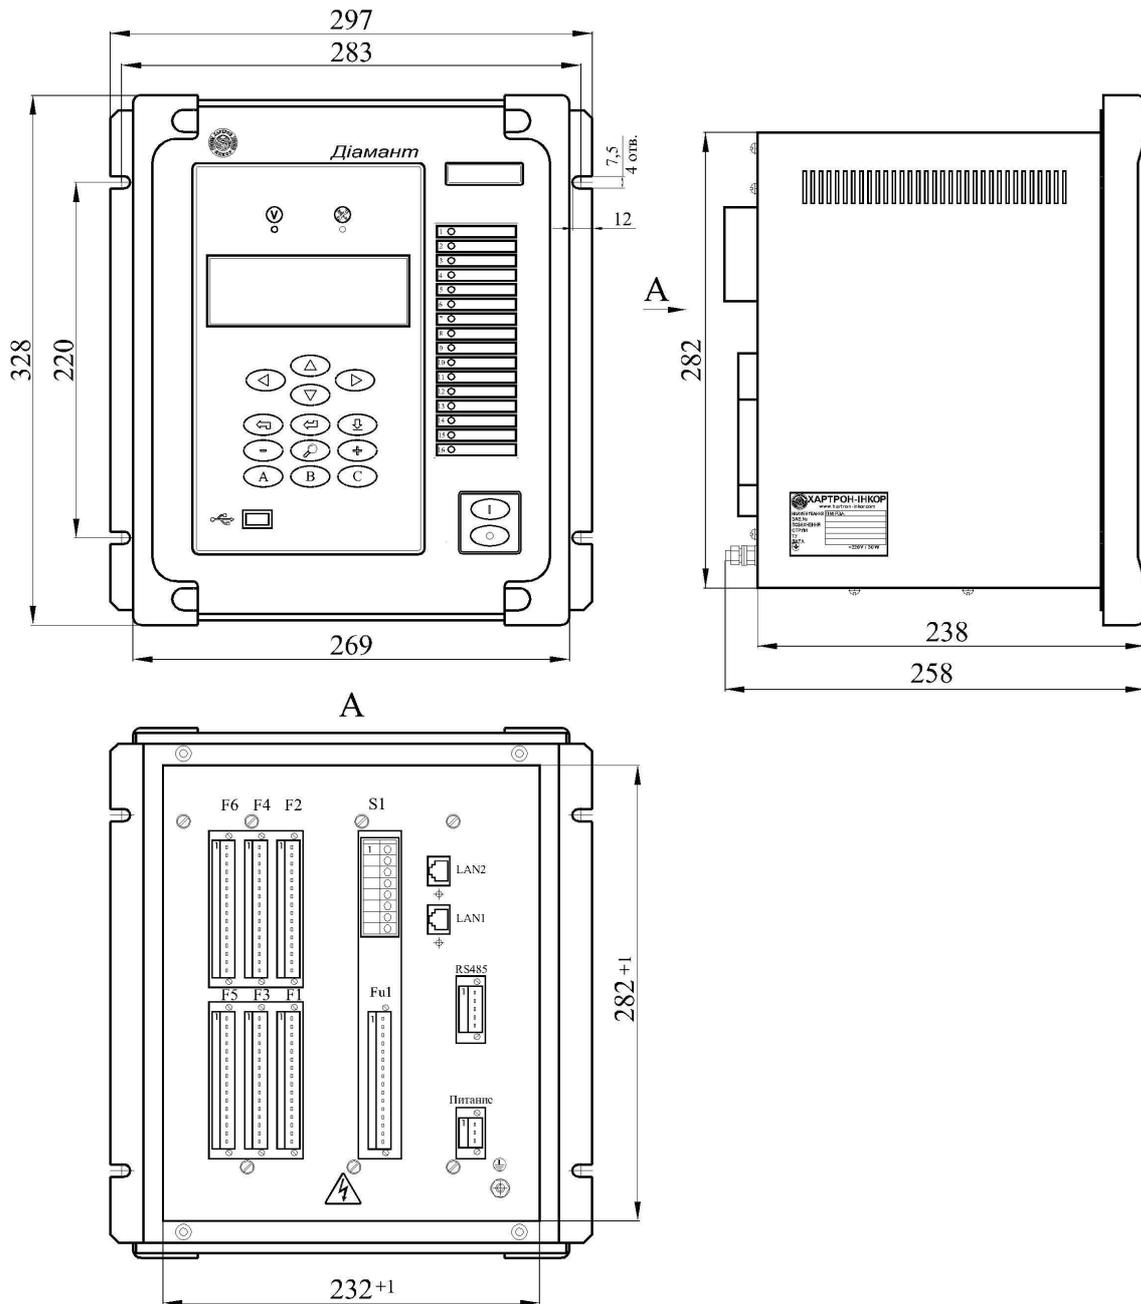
Габаритно – установочный чертеж ПМ Р3А
